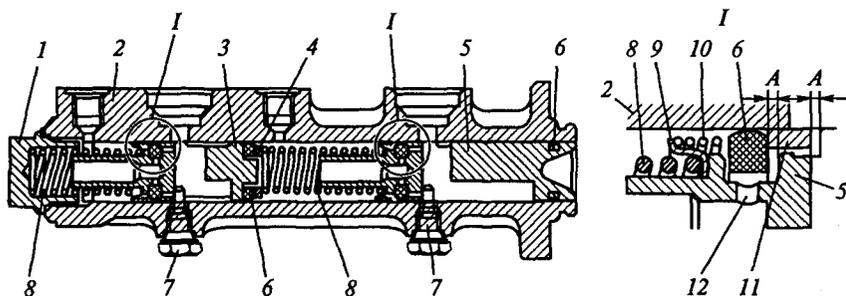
Главный цилиндр гидравлического привода тормозов:
